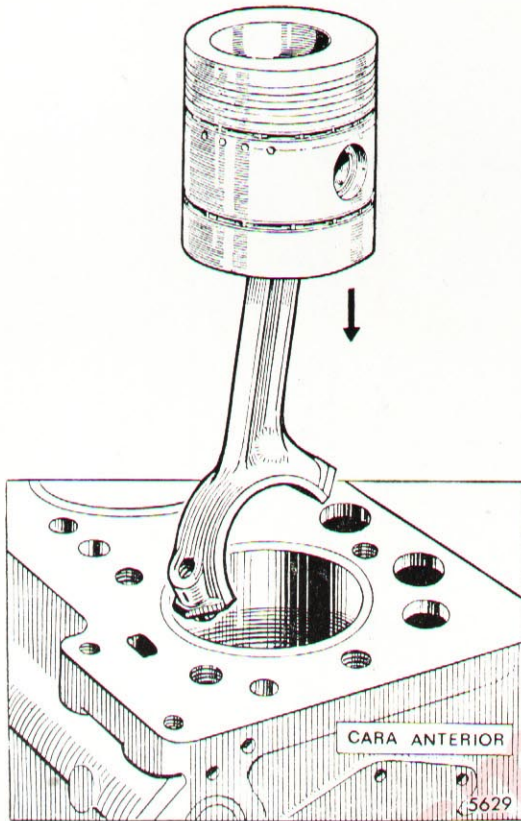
Posición de montaje del conjunto émbolo-biela sobre el bloque.
